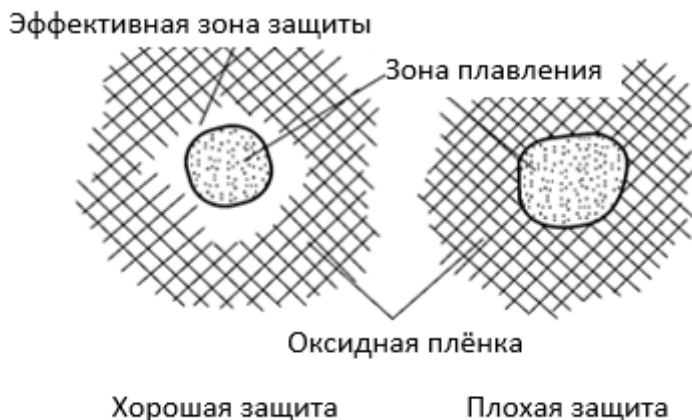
Влияния защиты аргона при сварке алюминия
